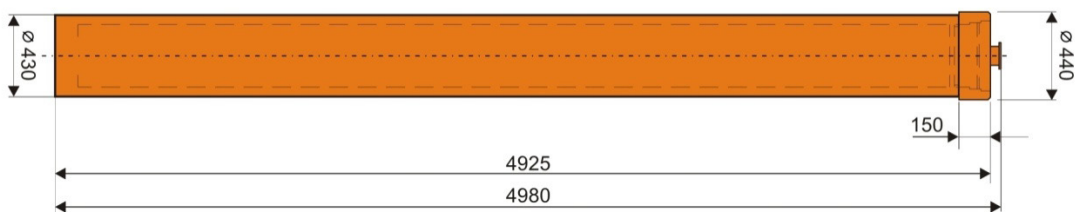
Technische Zeichnung einer BSK (Maßangaben in mm) /THO 09/
